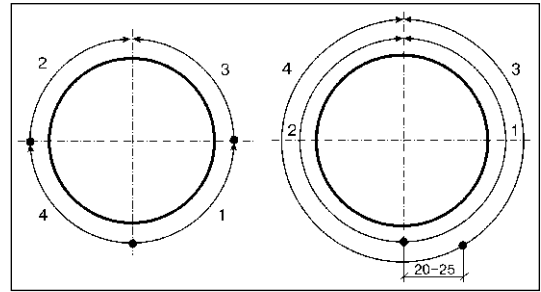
Порядок сварки неповоротного стыка: а — корневого шва; б — второго и последующих швов; 1-4 — последовательность наложения швов
